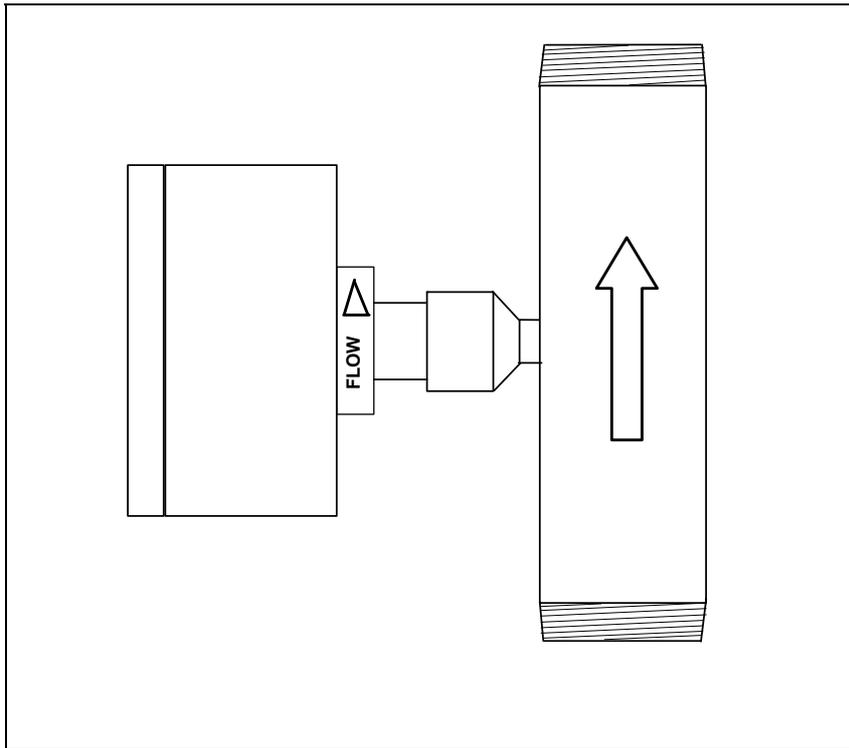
In-Line Sensor mit R oder NPT Gewinde und Strömungspfeil
